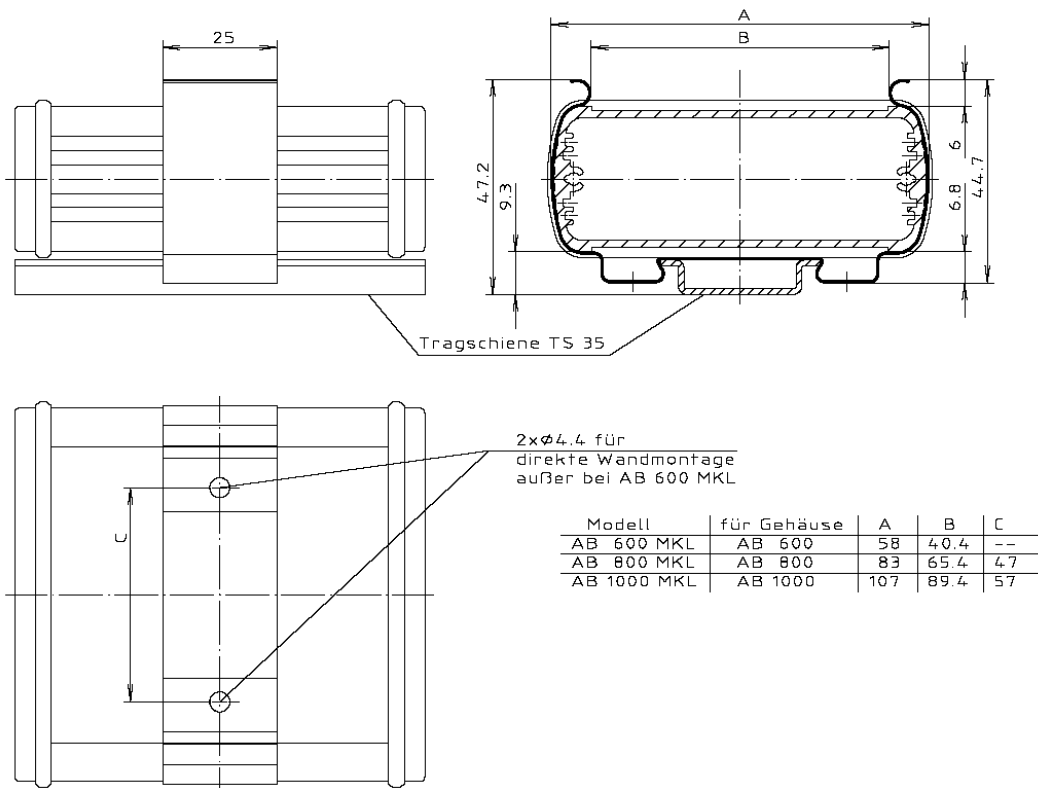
в. Чертеж скобы монтажной AB 800 MKL
